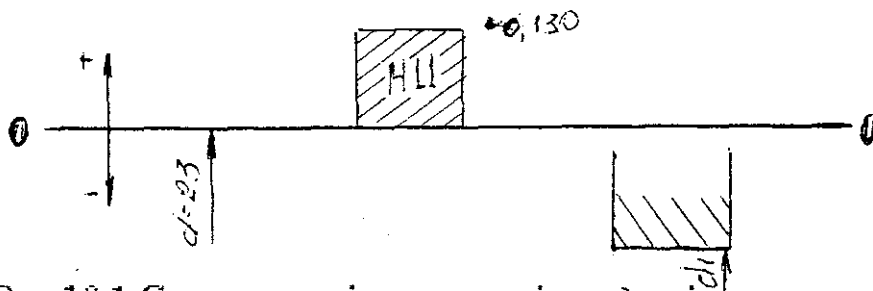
Схеми розміщення полів допусків для розміру d
